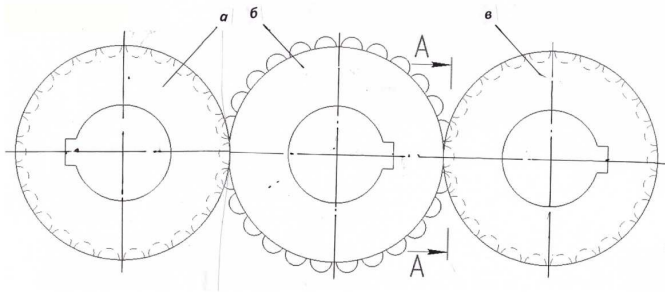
Схема цилиндрического зацепления роликовой передачи (ЦЗРП) в двухпарной гитаре цепи настройки металлорежущего станка: а и в – число впадин в сменных колесах со падинами под тела качения; б – число тел качения в промежуточном паразитной колесе с роликами ЦРП
